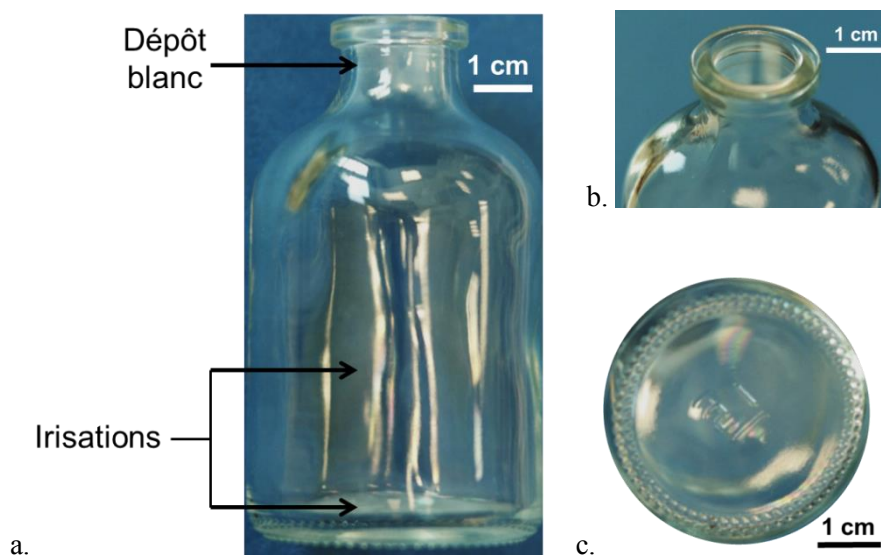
Dépôt 200-B. Photographies en vue de côté (a) en perspective (b) et en vue de dessous (c) du flacon revêtu.
